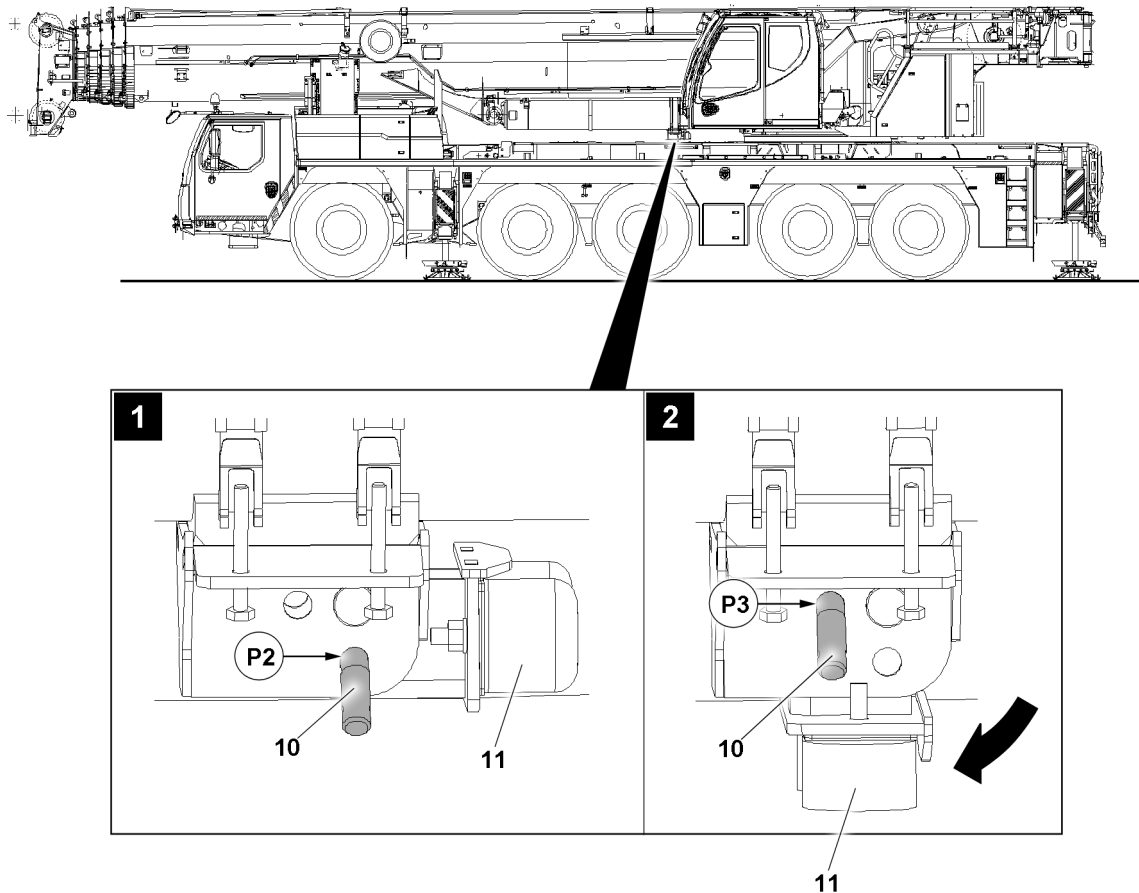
Rebater a patola do cilindro de basculamento para baixo
